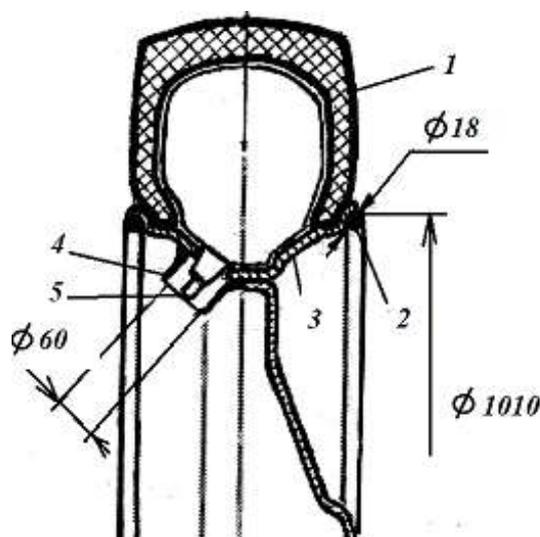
Схема восстановления диска заднего колеса МТЗ: 1 – шина; 2 – кольцо усиления; 3 – обод диска колеса; 4 – привариваемая цилиндрическая вставка; 5 – вентиль камеры
